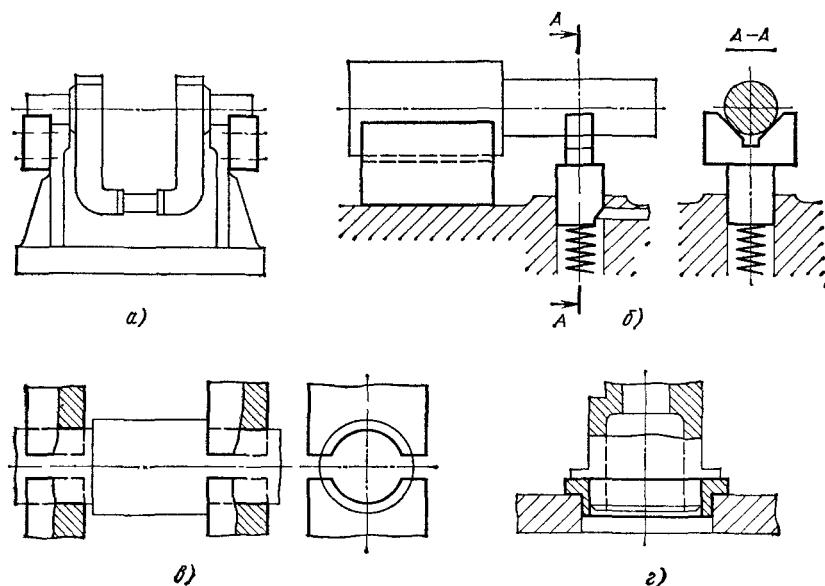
Примеры установки заготовок с наружной цилиндрической поверхностью:
